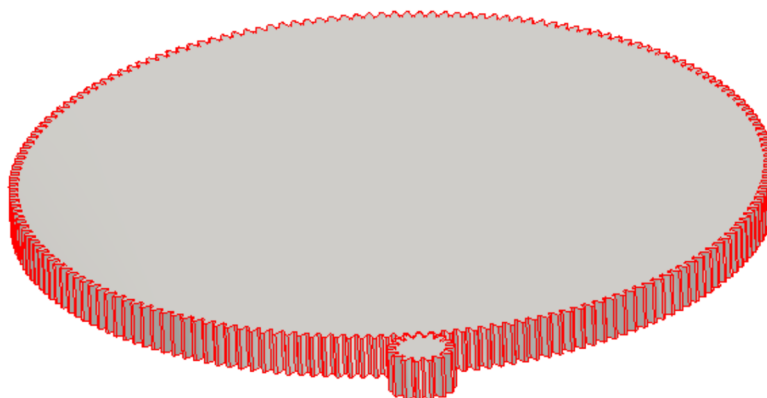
Загальний вигляд циркулярної роботизованої парковки
